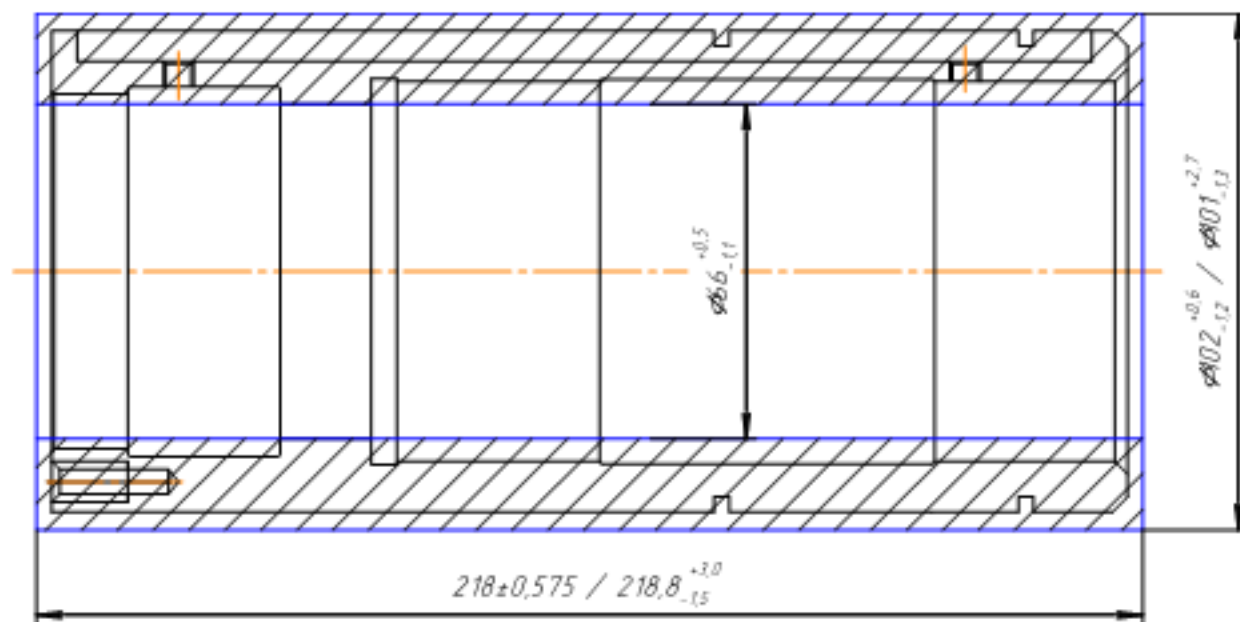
Ескіз заготовки виготовленої з прокату / виготовленої штампуванням
